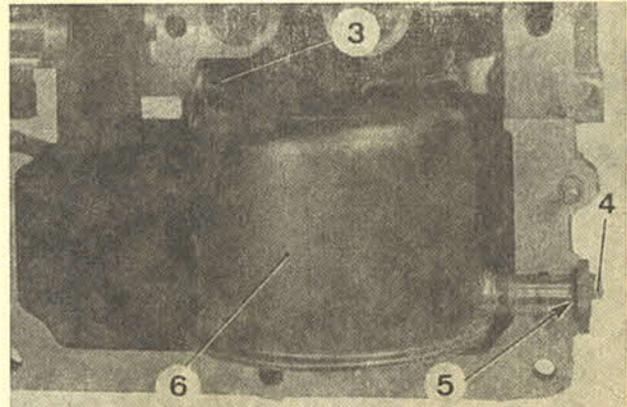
Filterpatrone mit O-Ring in Einbaulage
